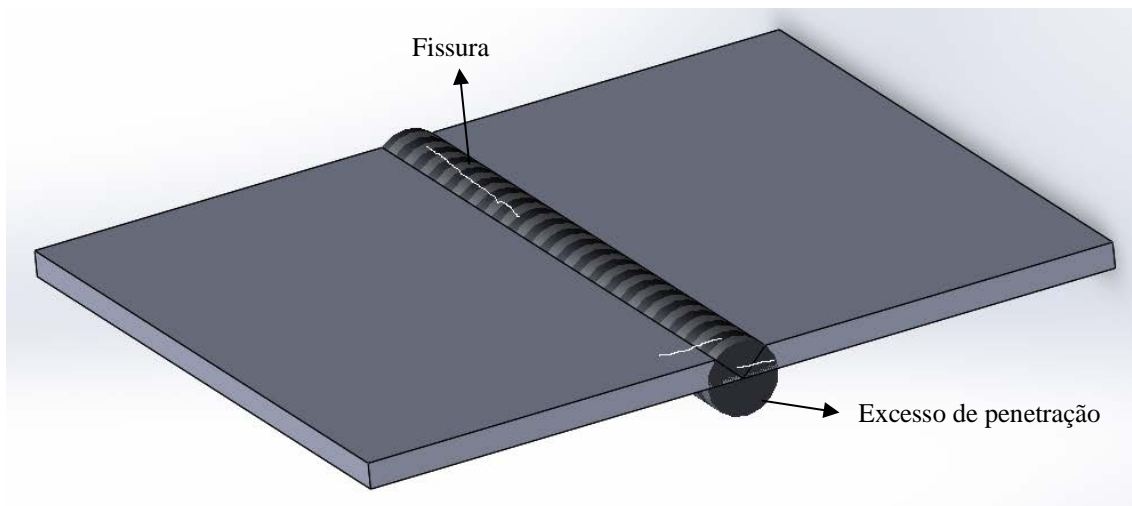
Ilustração sobre alguns defeitos no cordão de soldadura.
